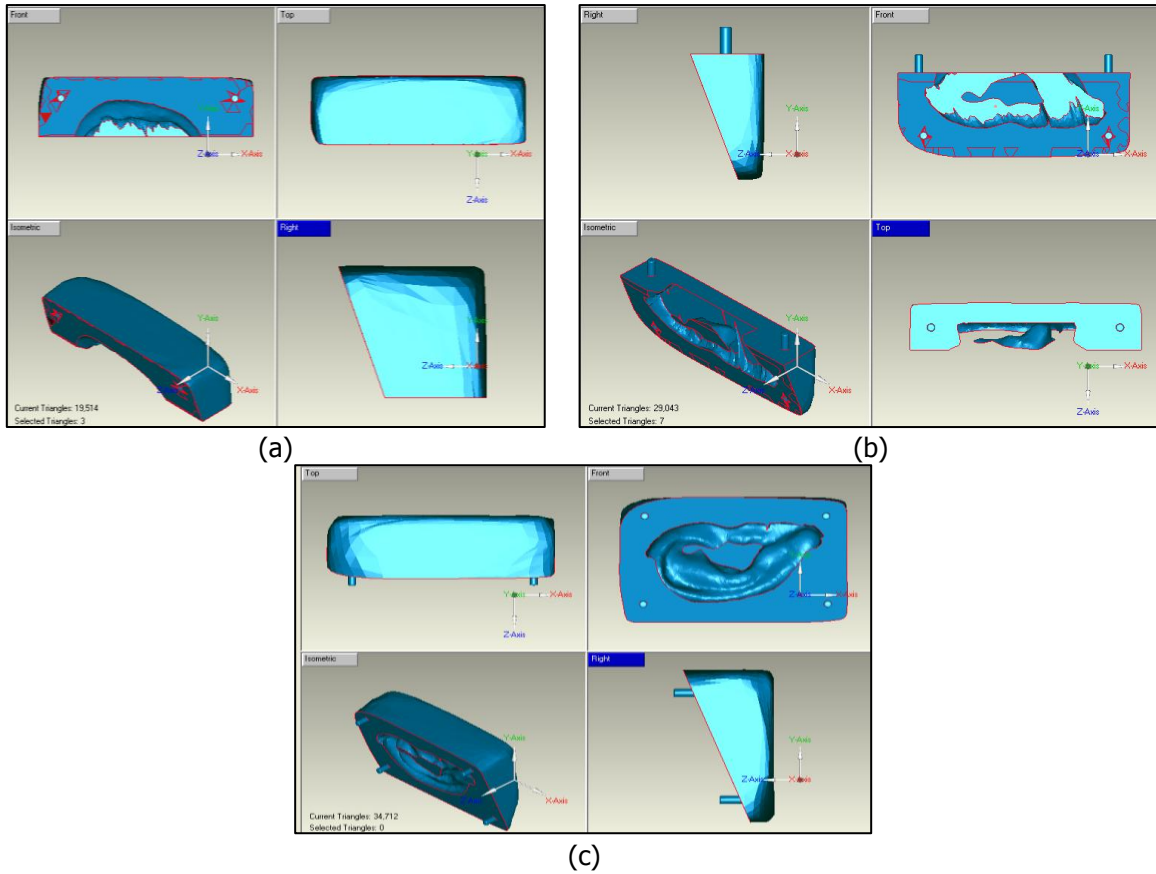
(a) Molde inferior 1, (b) molde inferior 2, (c) molde superior.
